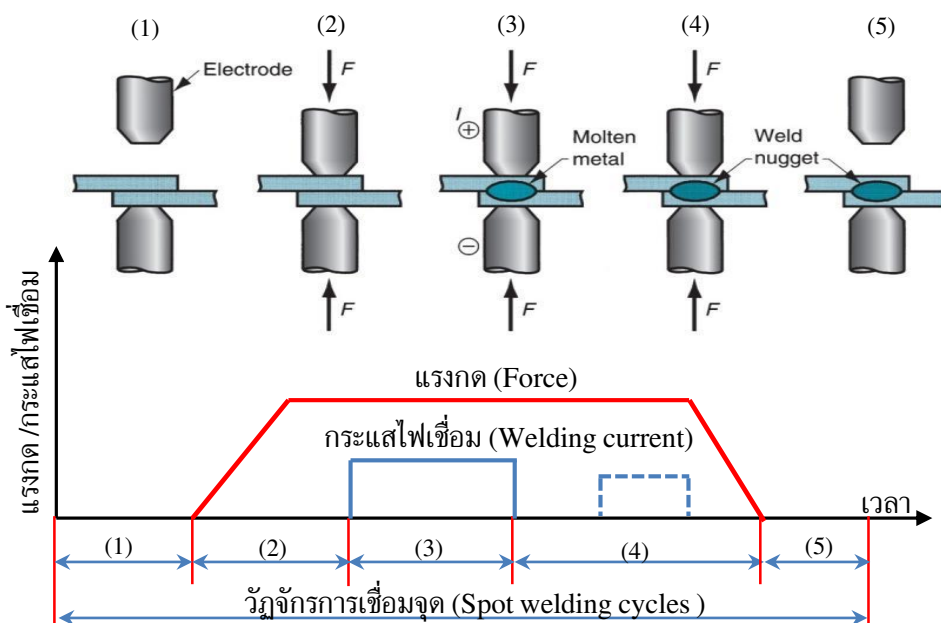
กลไกระบบของการเชื่อมความต้านทานแบบจุด (Resistance spot welding)
